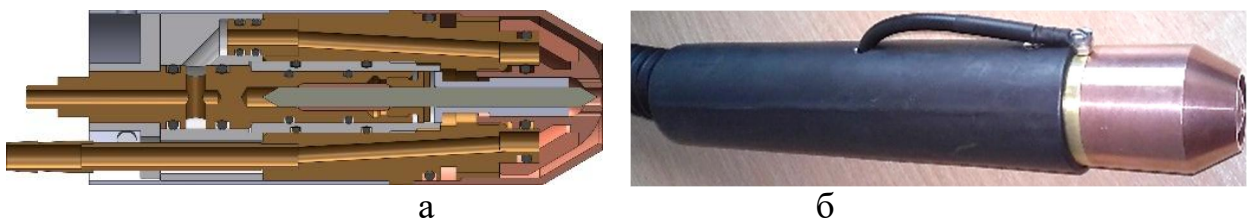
Комп'ютерна модель (а) та зовнішній вигляд (б) універсального плазмотрону для точкового та шовного зварювання.
